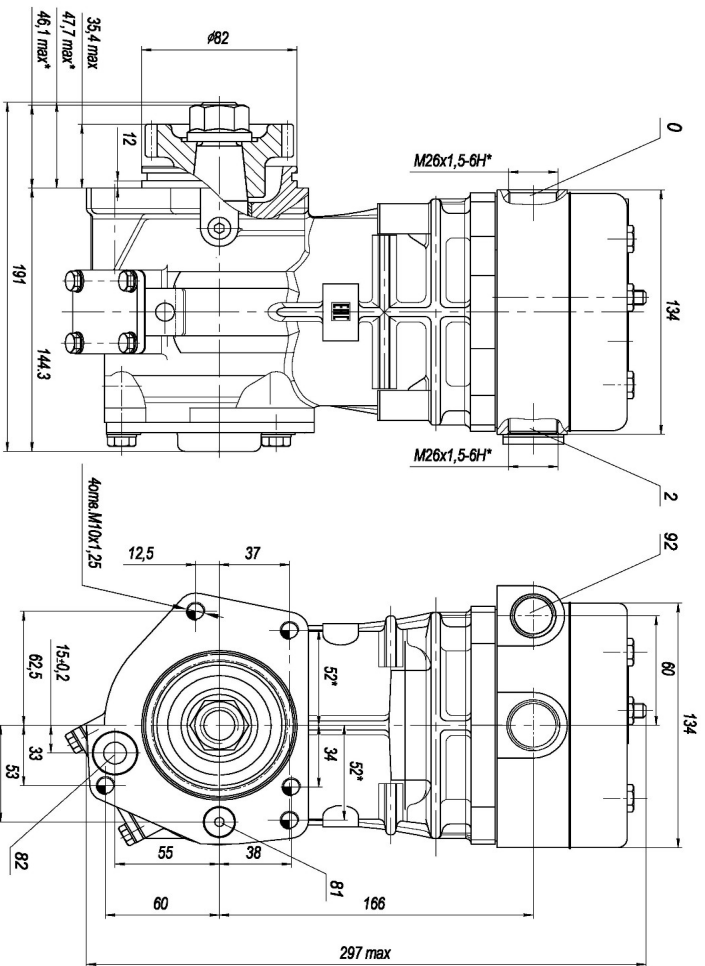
Присоединительные и установочные размеры компрессора АМ.3509015-03.
